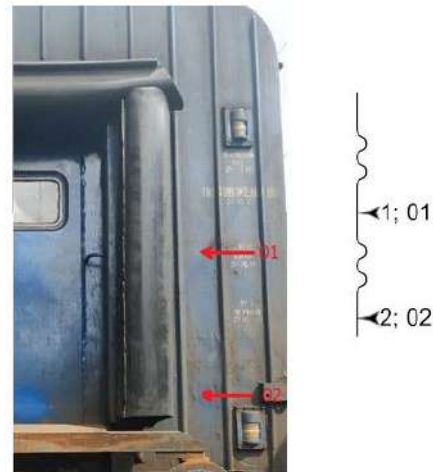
Схема проведення вимірювань обшивки торцевої стіни
